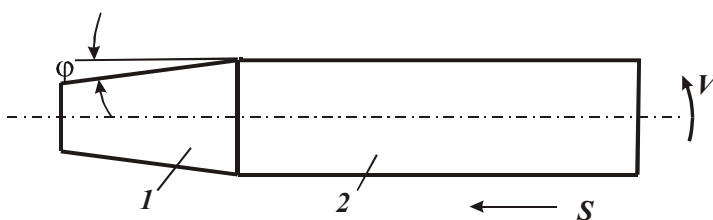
Принципова схема конструкції осевого багатолезового інструмента для обробки отвору: 1 – забірна частина; 2 – калібруюча частина
